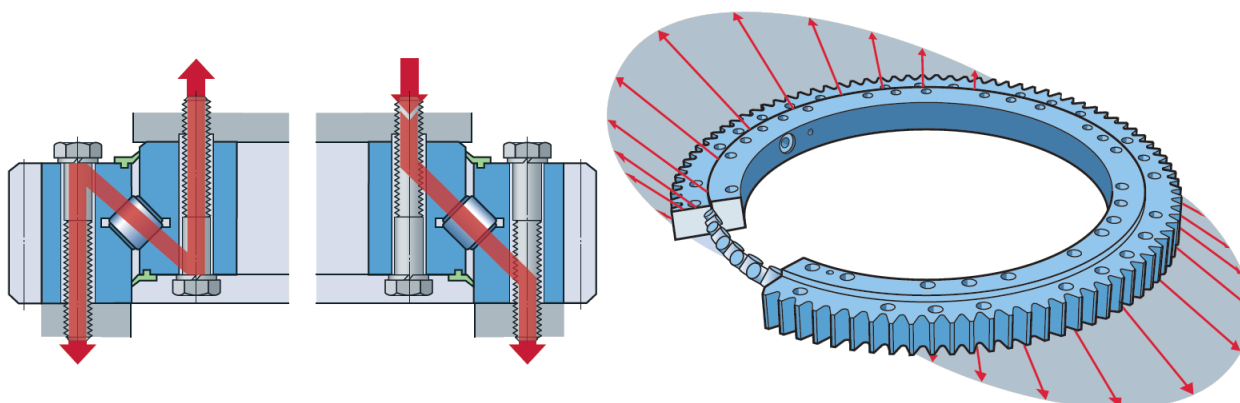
Záporné axiální zatížení ložiska se zkříženými válečky [3]
